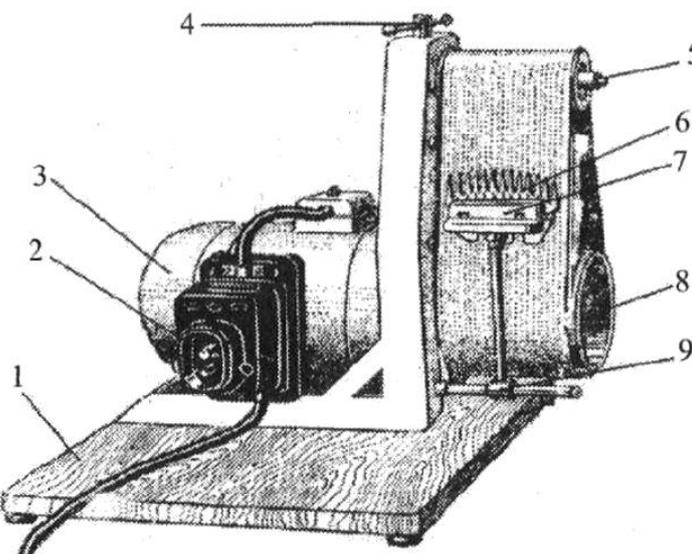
Стрічковий точильний апарат: 1 - підстава; 2 - вимикач; 3 - електродвигун; 4 - гвинт натяжного пристрою; 5 - натяжний ролик; 6 - гребінка, що заточується; 7 - державка; 8 - провідний шків; 9 - поворотна втулка стійки державки (на кронштейні).
